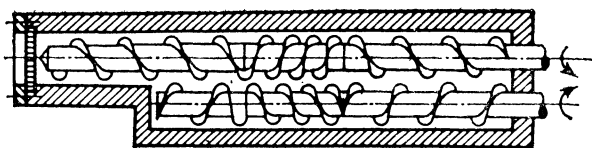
Схема двухчервячного пластосмесителя фирмы Welding Engineers (США).
